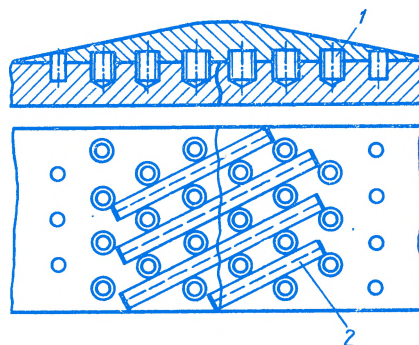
Расположение стальных связей в металле шва при холодной сварке чугуна: 1 – шпильки, 2 – стальные связи
